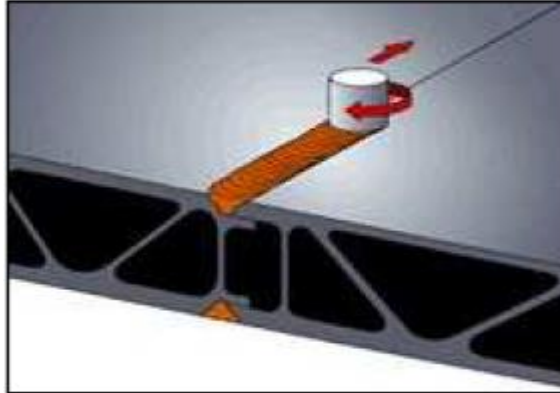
Technique de soudage des carrosseries des trains Hitachi [9].
